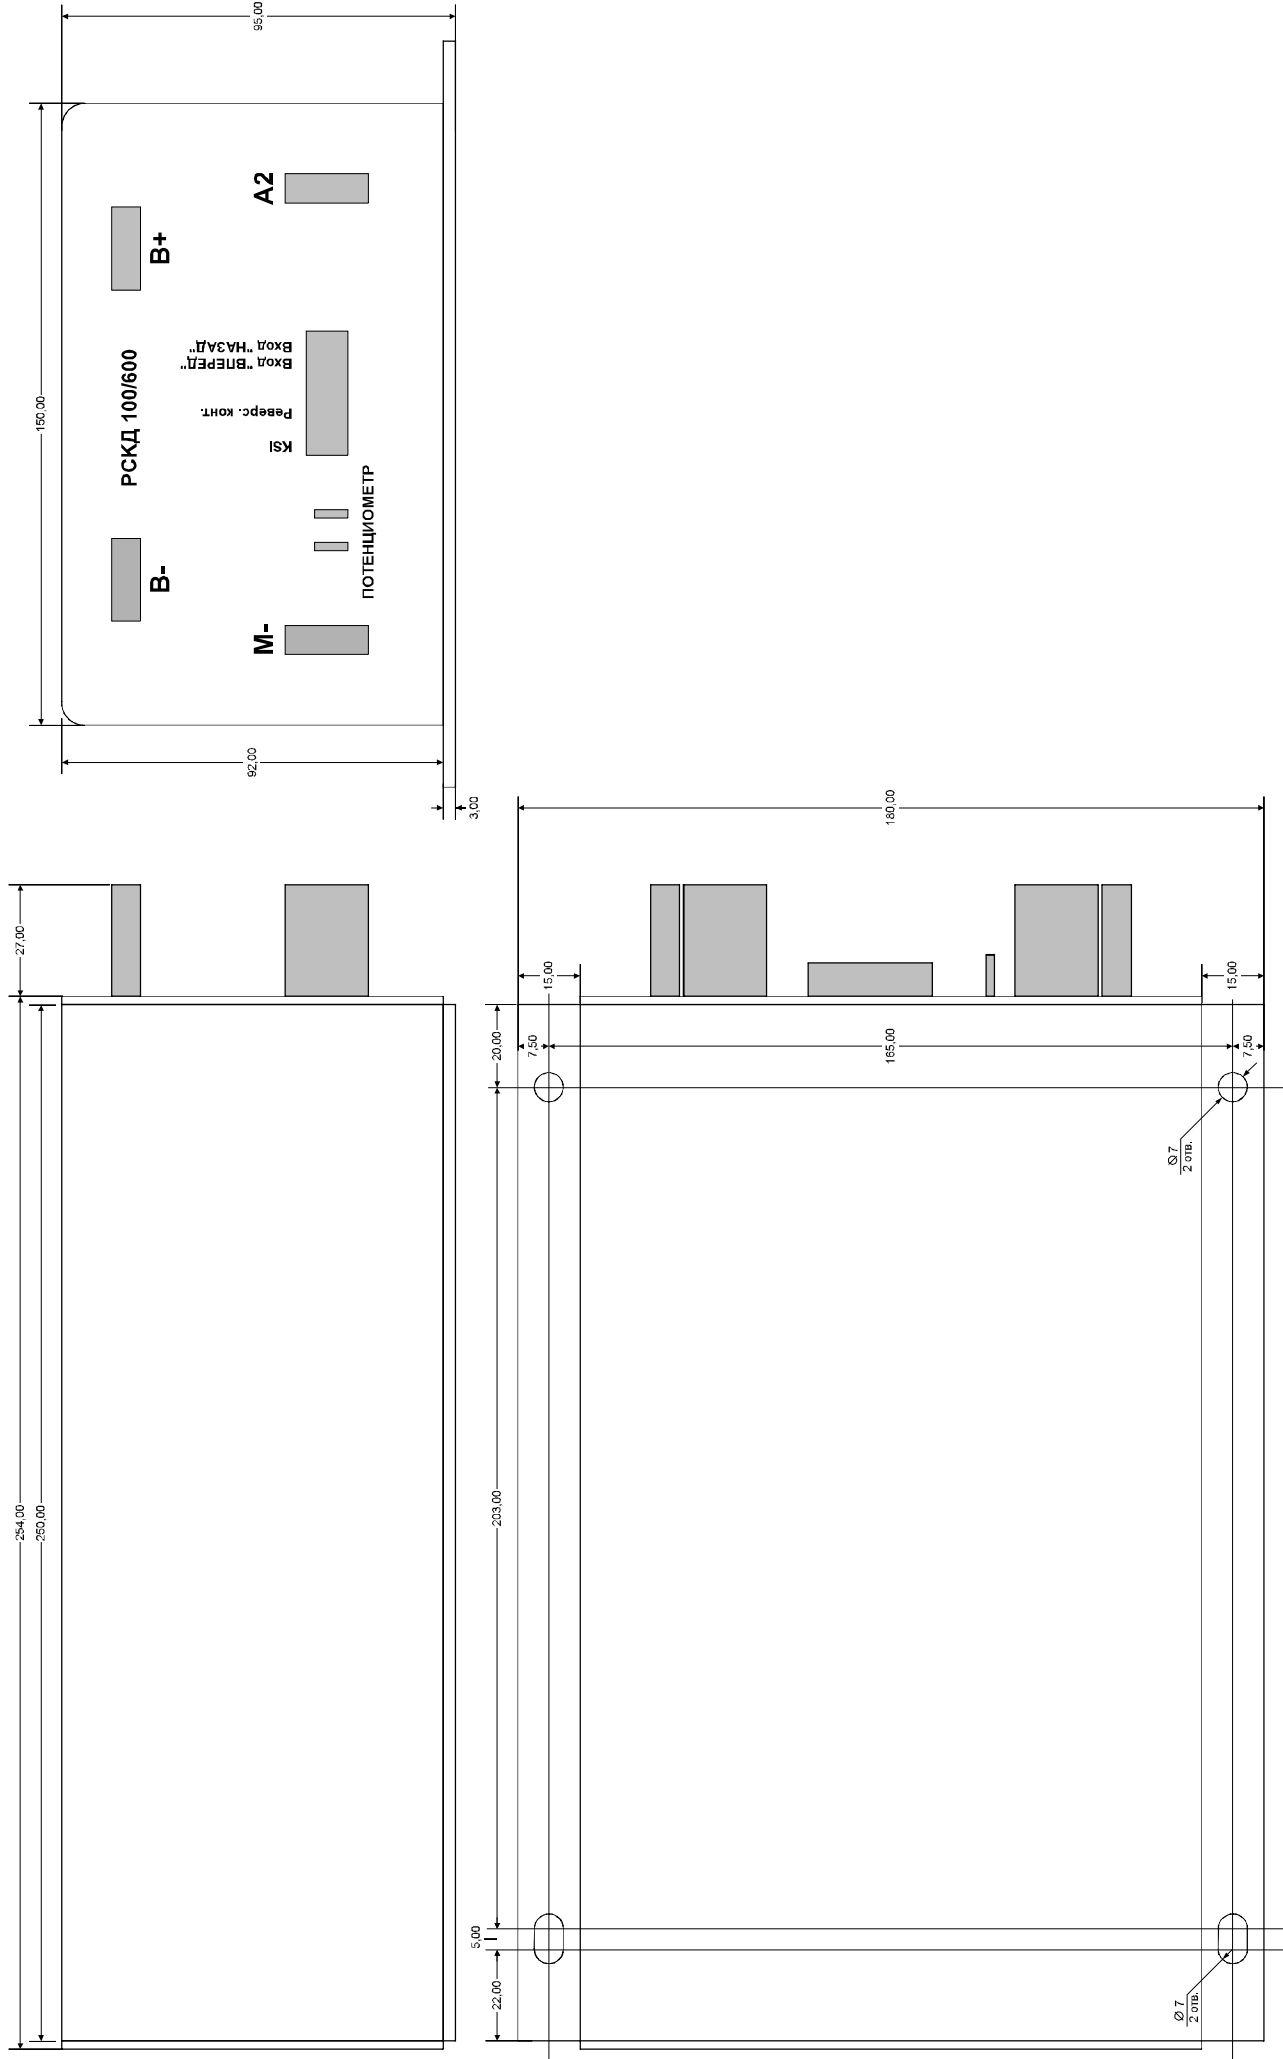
Чертеж РСКД 100/600 с указанием габаритных размеров
